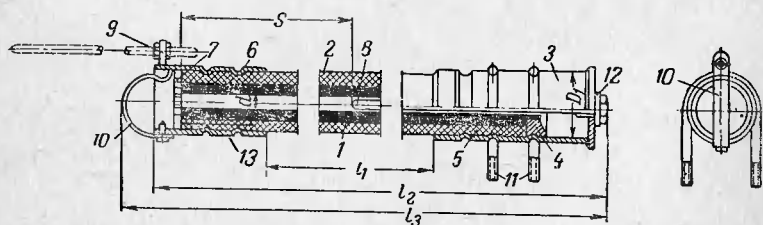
Конструкция фибробакелитовых трубчатых разрядников серии РТФ.
